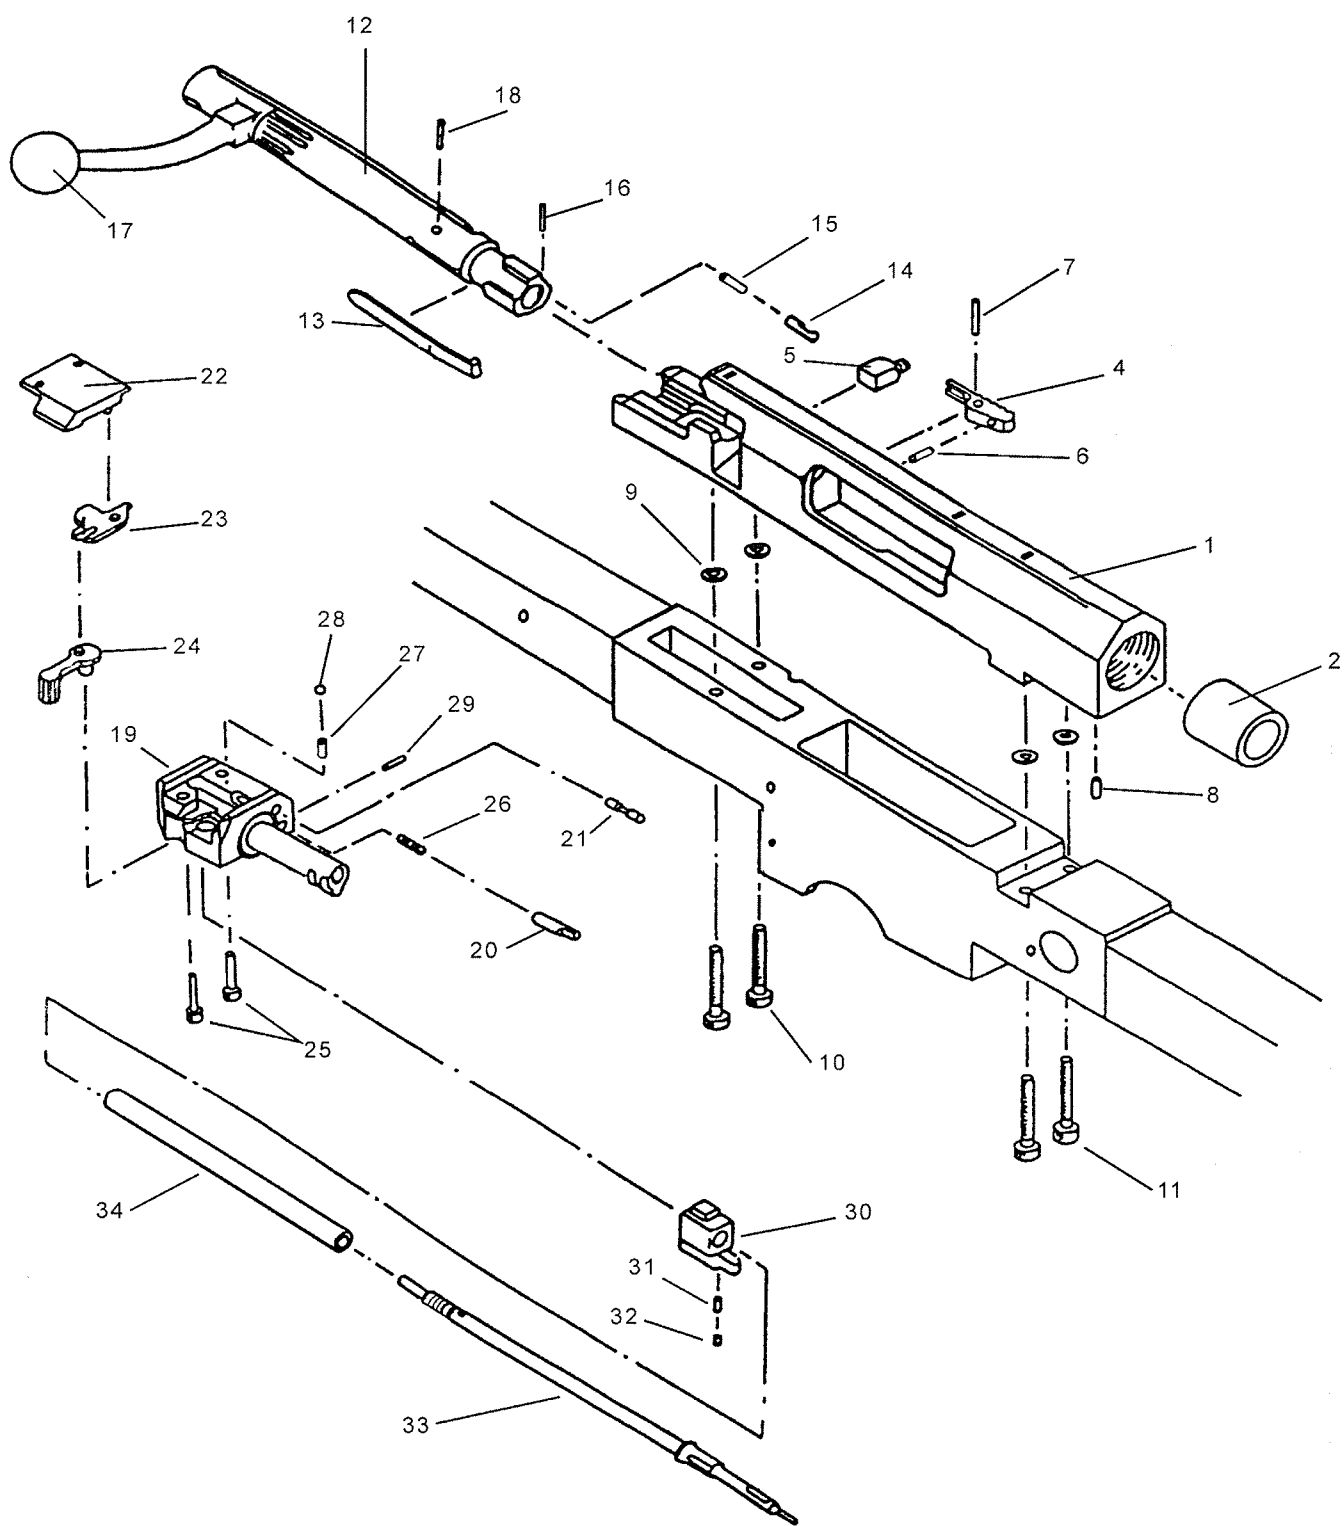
Conjunto de cajón de mecanismos, cerrojo y tapa
